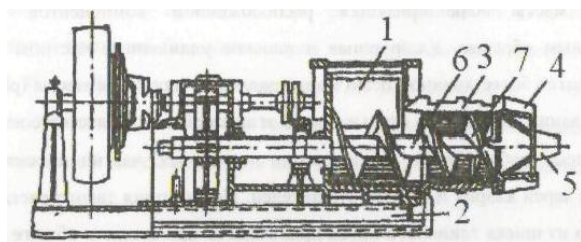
Ленточный безвакуумный пресс СМ-294: 1 - приемный люк; 2 - станина; 3 - корпус; 4 - головка; 5 - мундштук; 6 - вал; 7 - лопасть винта
